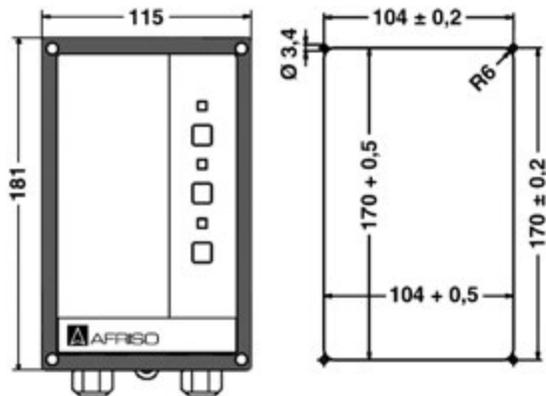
Messumformer mit Montagerahmen für den Einbau in Schalttafeln;
